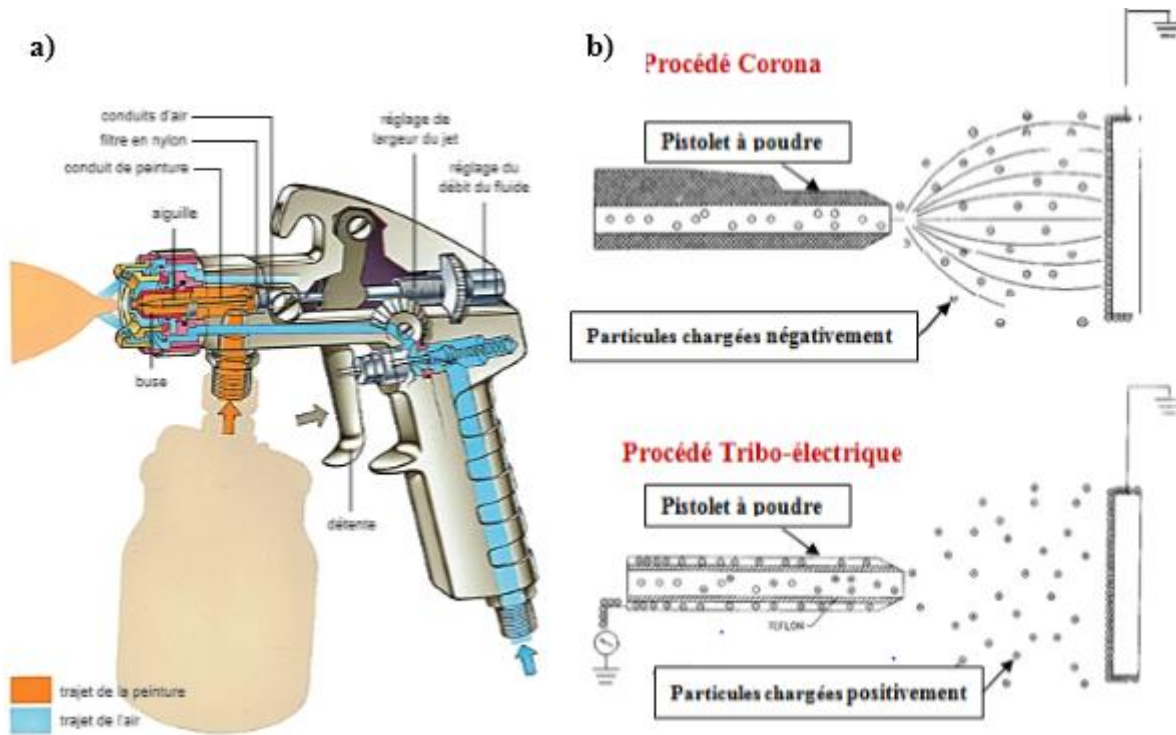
Pistolet à peinture : (a) pistolet pneumatique, (b) pistolet électrostatique : procédé corona et procédé tribo-électrique [73]
